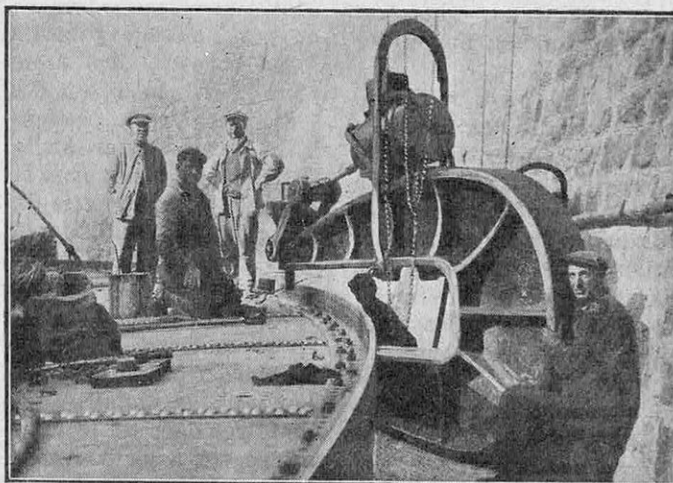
PRESSE PNEUMATIQUE A RIVER
